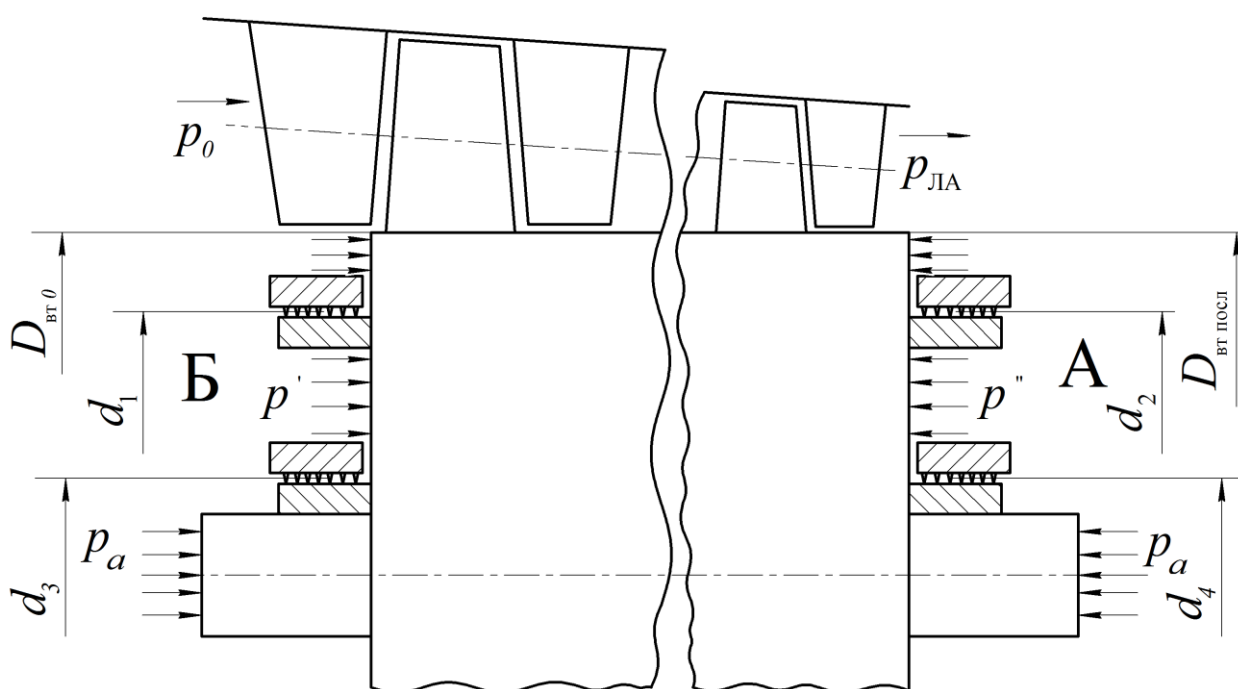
Схема для определения осевых усилий на торцевых поверхностях ротора осевого компрессора авиационного двигателя
